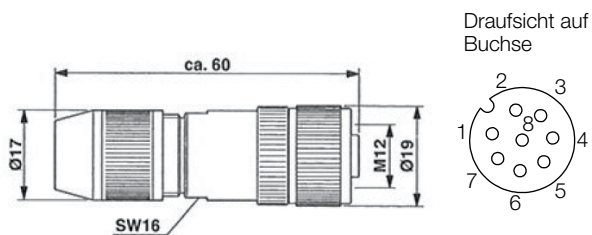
Steckverbinder BCC M478-0000-1A-000-43x834-000
